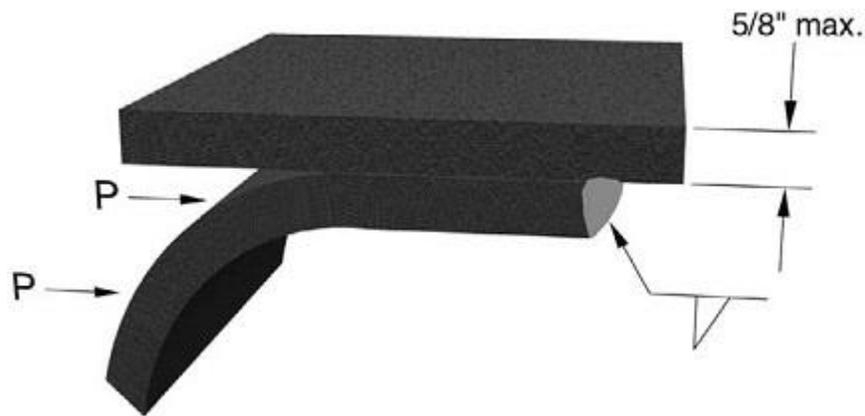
Unión por soldadura cascarón-tapa de tipo 6.
